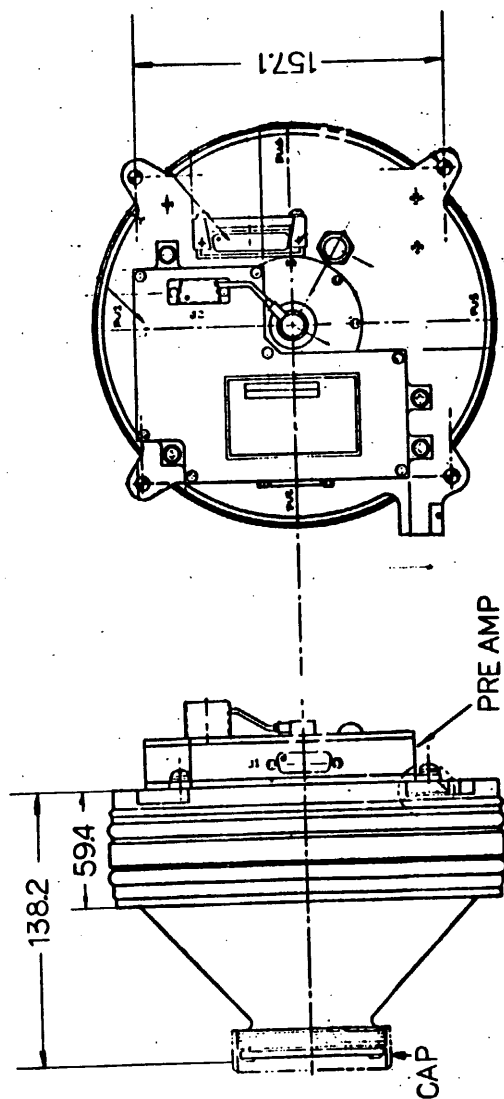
SWA(SCAN WHEEL ASSEMBLY) 外觀図
